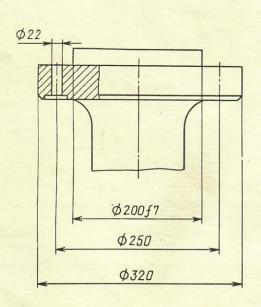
Габаритные размеры рабочего пространства станка 273311*H
